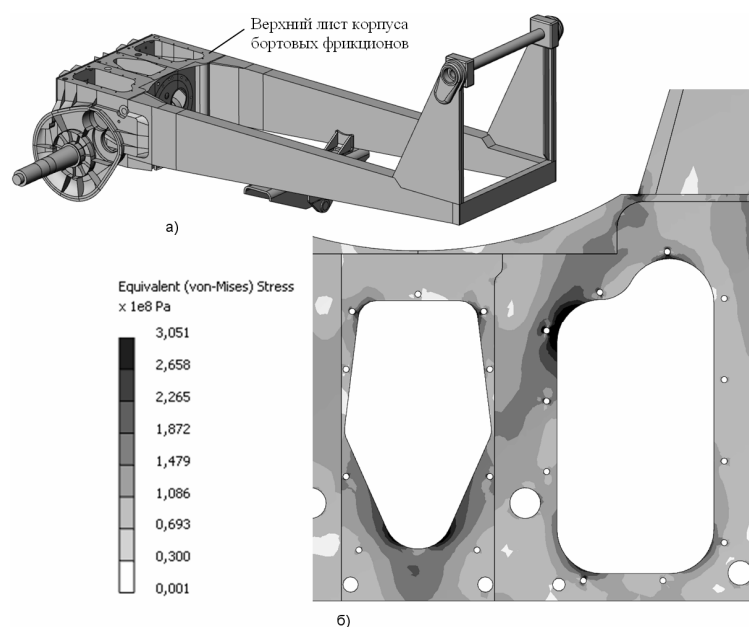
Внешний вид рамы промышленного трактора Т10 (а); фрагмент поля напряжений в верхнем листе корпуса бортовых фрикционов (б)
